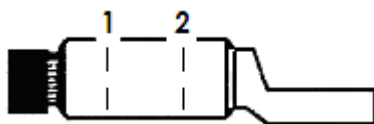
Ordem de punçõagem dos terminais bimetálicos
